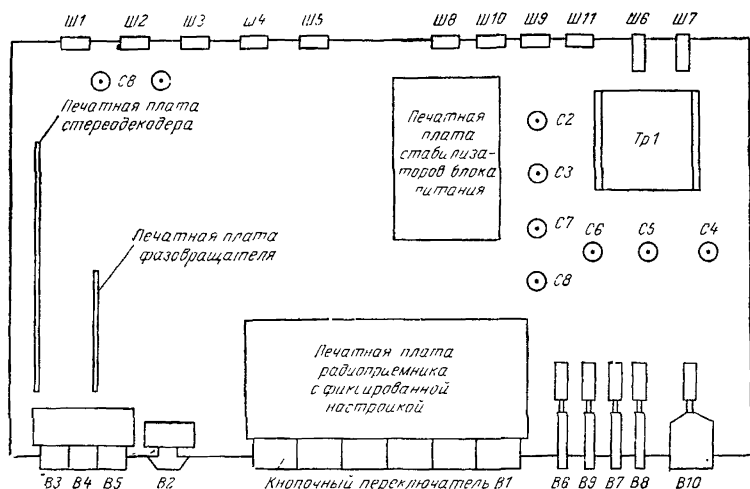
Расположение деталей усилителя (вид со стороны подвала шасси).
